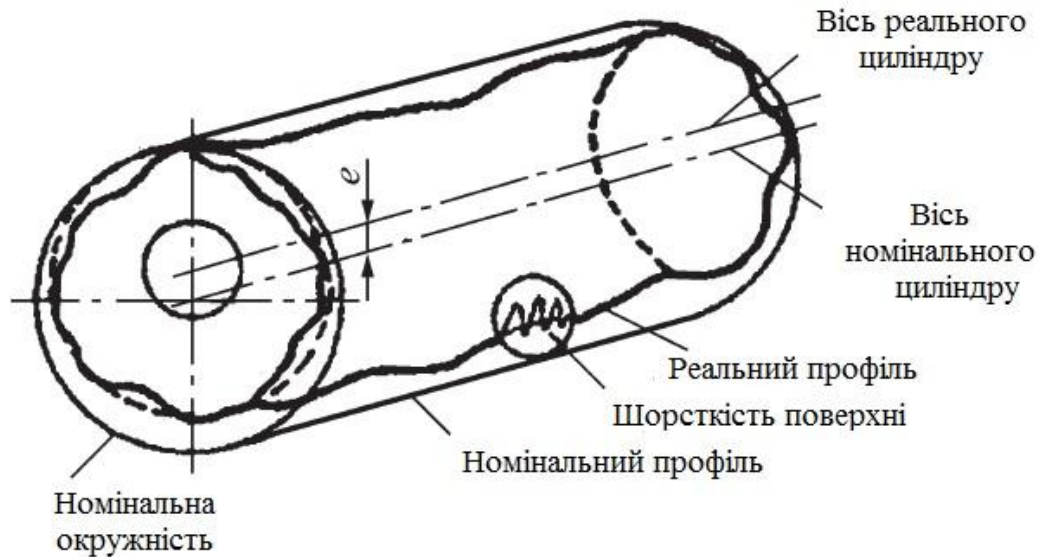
Спотворення розмірів та форми циліндру після виготовлення:
